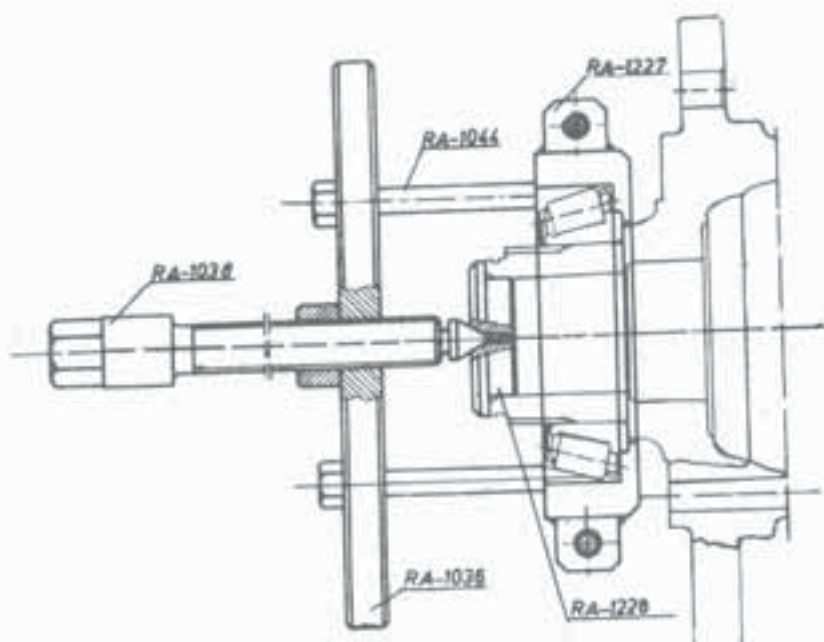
Выпрессовка наружного кольца конического роликоподшипника
